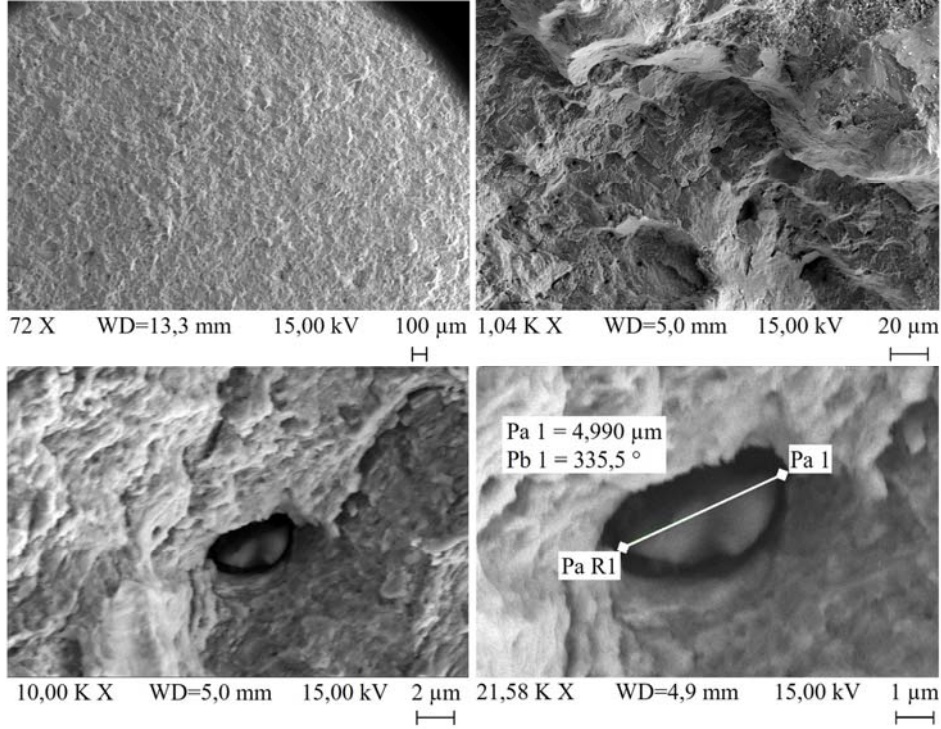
Yorulma testi sırasında kırılan çatalı flanş parçasına ait görsel (Fractured flange yoke during fatigue test).
